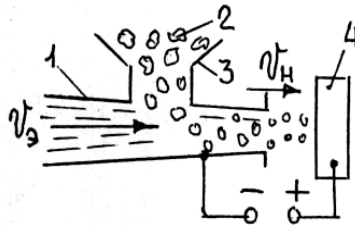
Схема подавання наповнювача до заготовки: 1 – сопло; 3 – дозатор; 2 – наповнювач; 4 – заготовка
